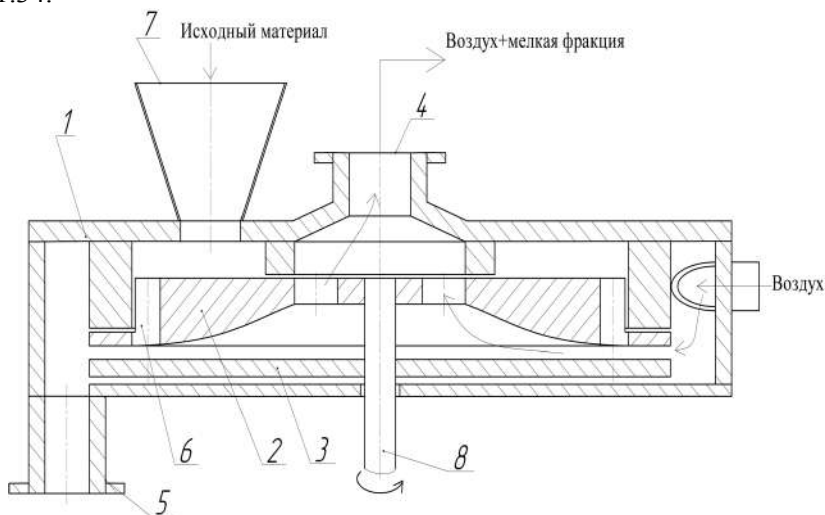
Воздушно-центробежный насыпной классификатор конструкции кафедры МиАХП СПбТИ (ТУ): 1 – корпус; 2, 3 – диски; 4 – выход воздуха; 5 – выход крупного продукта; 6 – распределительные каналы; 7 – подача исходного материала; 8 – вал.
